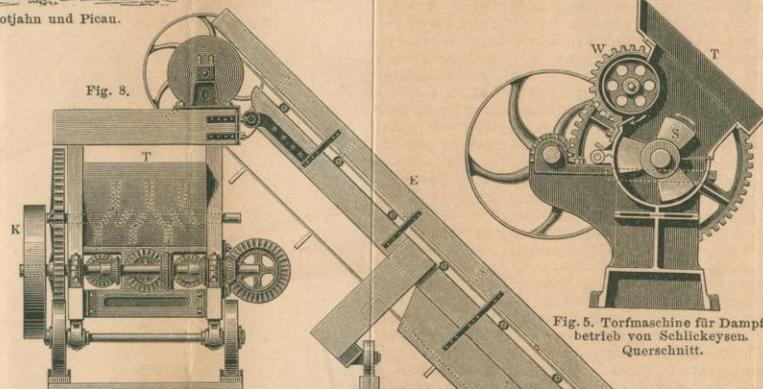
Torfmaschine für Dampftrieb von Schlickeysen. Querschnitt.
